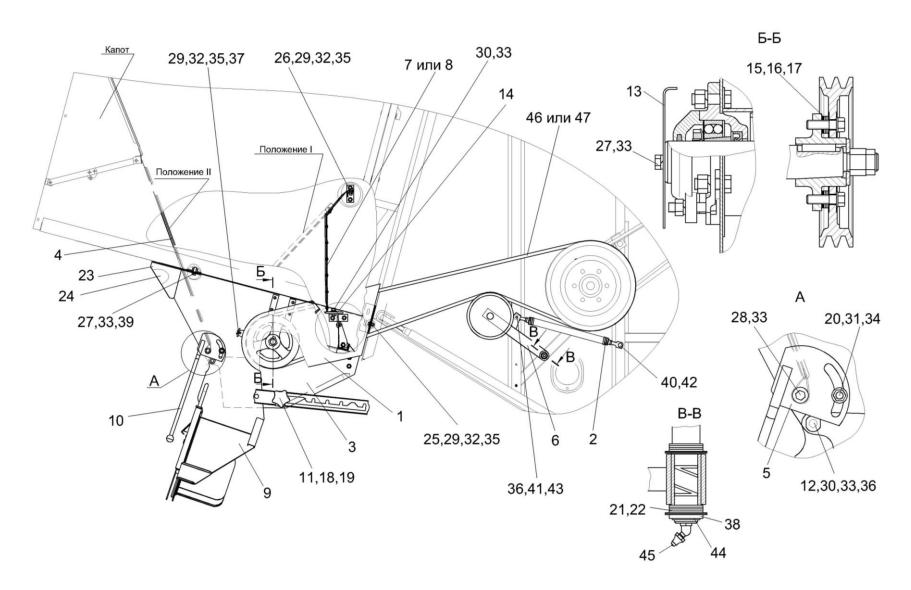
Установка соломоизмельчителя КЗК 0290600
